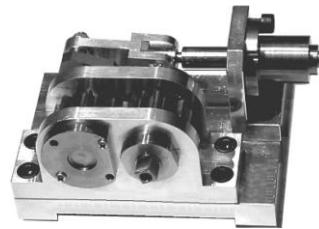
测绘对象——齿轮传动偏心滑块机构
